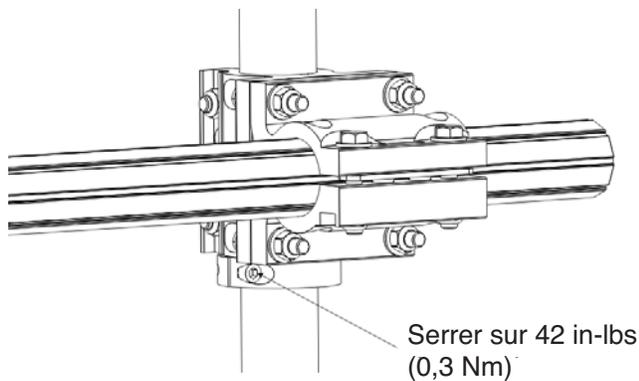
B – DISPOSITIFS DE SERRAGE
